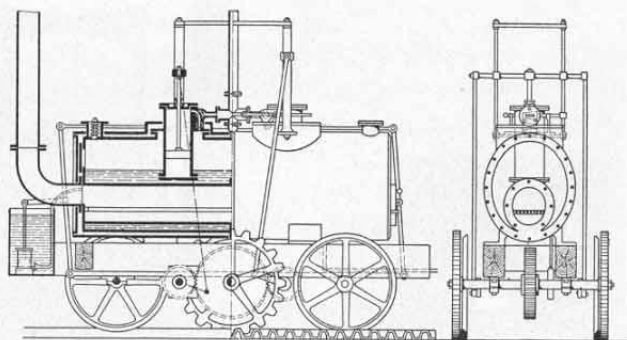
und 714. Blenkinsops Zahnradlokomotive 1811.
